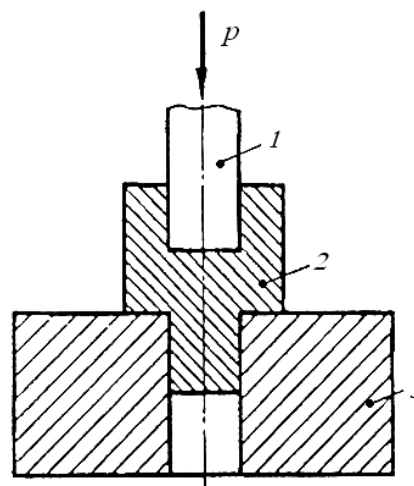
Схема приспособления для испытания на сдвиг круглых образцов: 1 – пуансон; 2 – образец; 3 – основание
